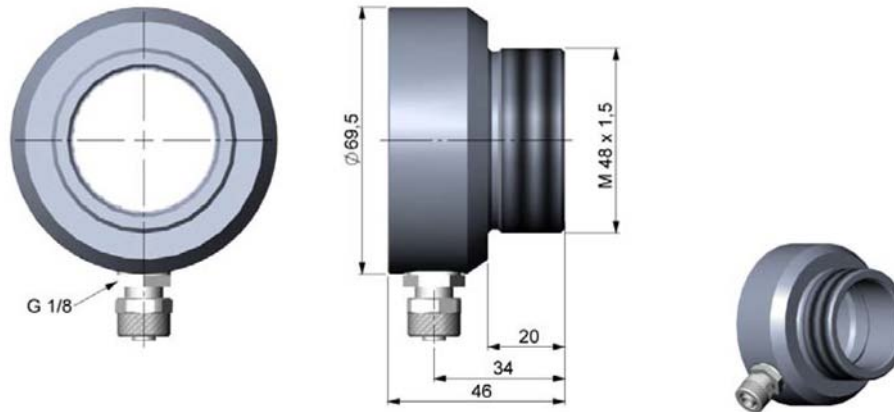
Freiblasvorsatz (TM-AP-CTL), Schlauchanschluss: 6x8 mm, Gewinde (Fitting): G 1/8 Zoll
